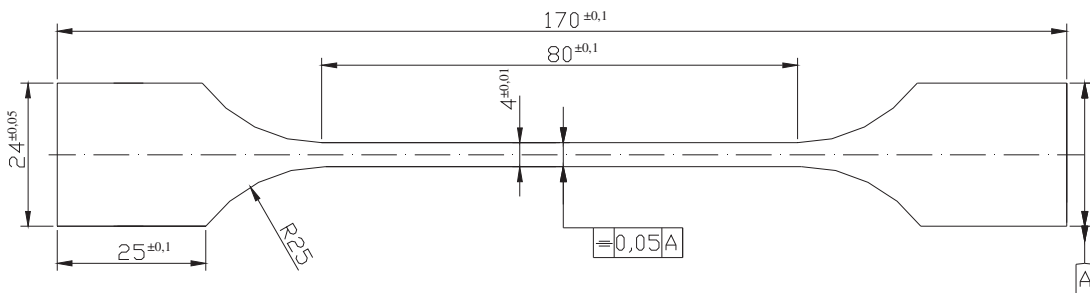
Epreuve plate prismatique avec section carré (4x4 mm).
